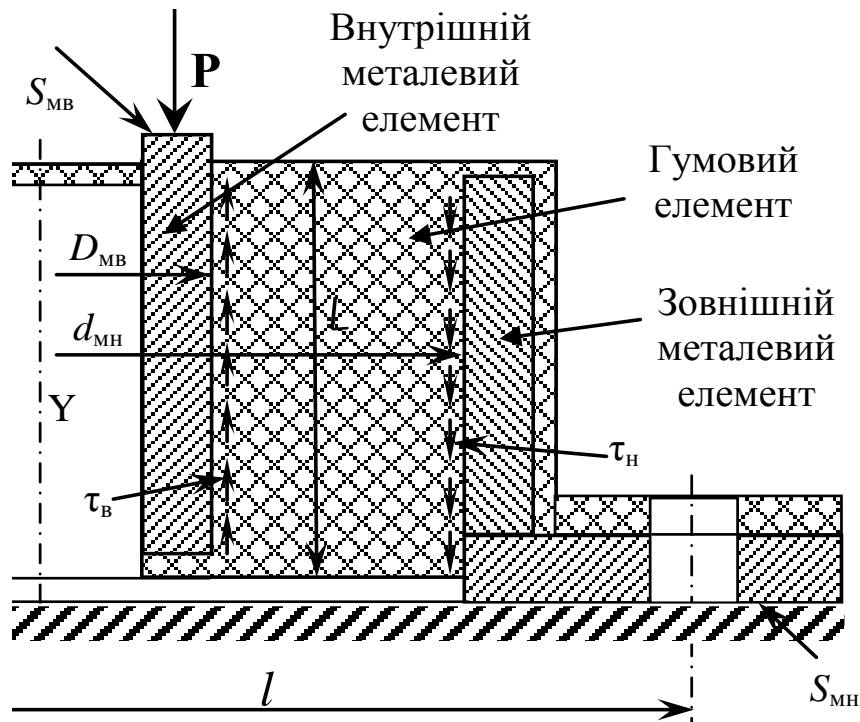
Розрахункова схема конструкції гумометалевого амортизатора АКСС-10 М
